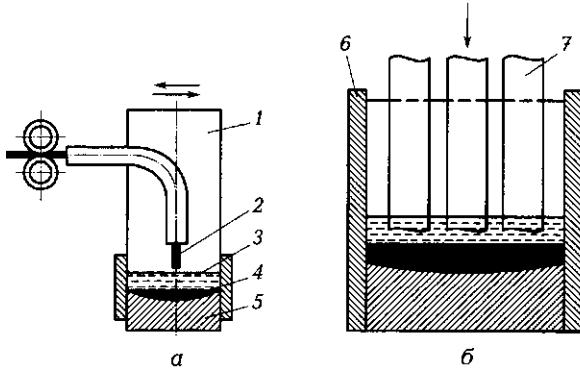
Процессы электрошлаковой сварки:
